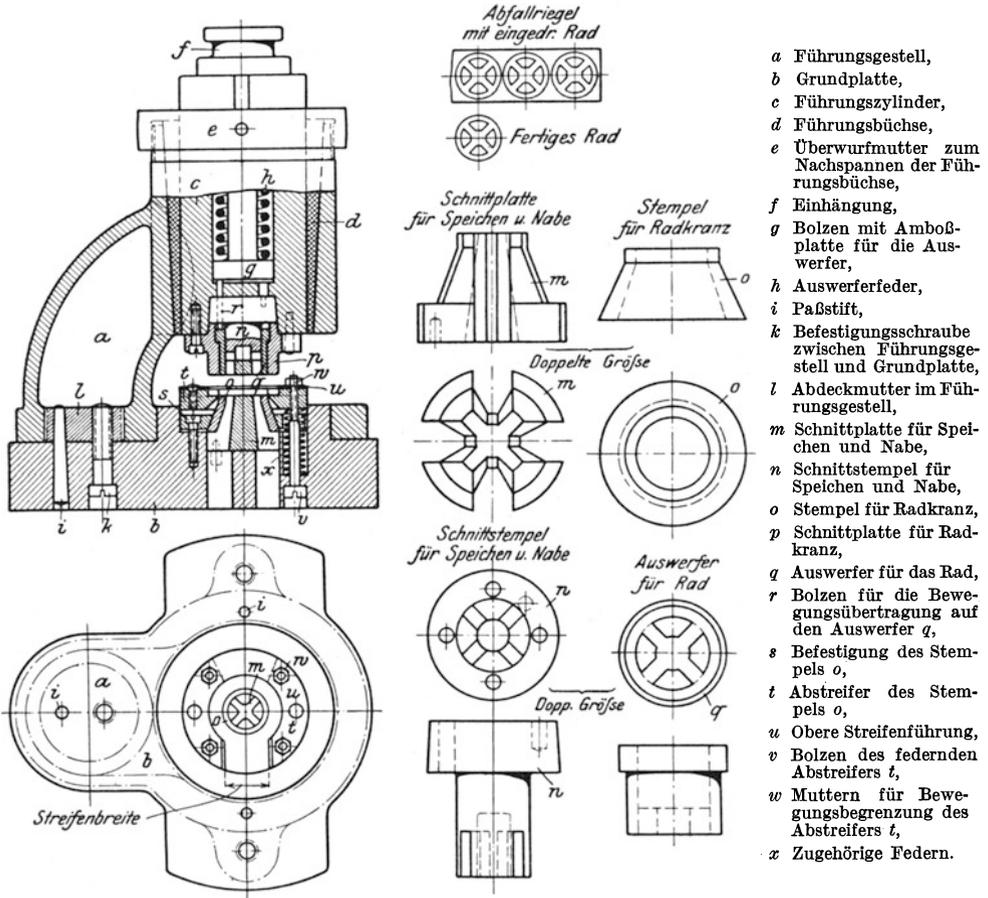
Verbundschnitt mit Blockführung, einfach ausgelegt.
